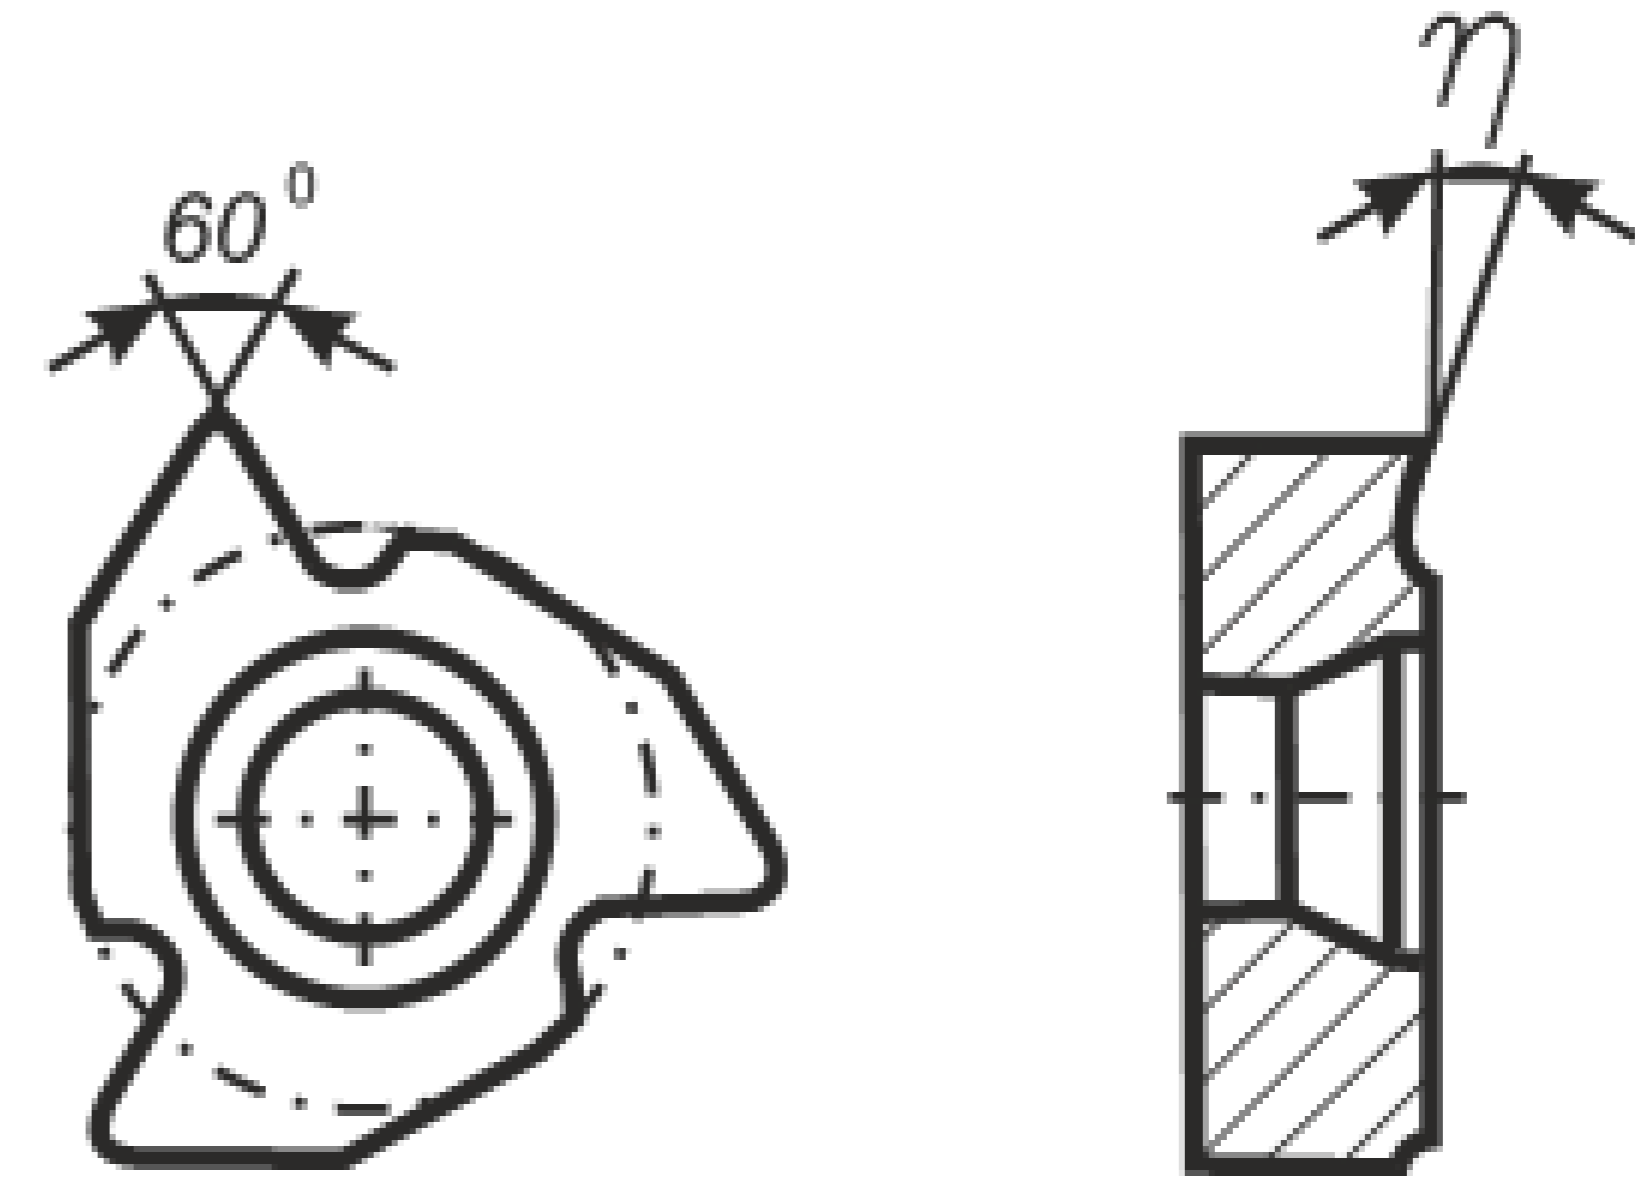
Нарізева права пластина фірми ZCC-CT для виготовлення нарізи за стандартом API 7
